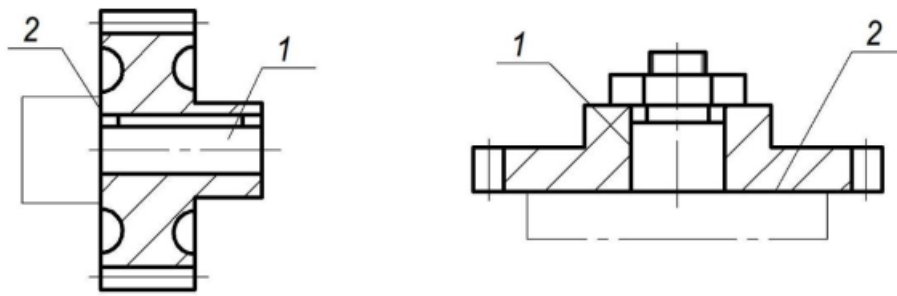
Схема основних конструкторських (а) і технологічних (б) баз зубчастих коліс: 1 – базовий отвір колеса; 2 – базовий торець колеса
